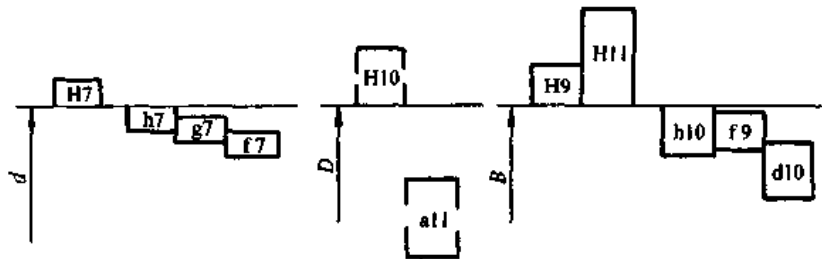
一般用途矩形花键的尺寸公差带
